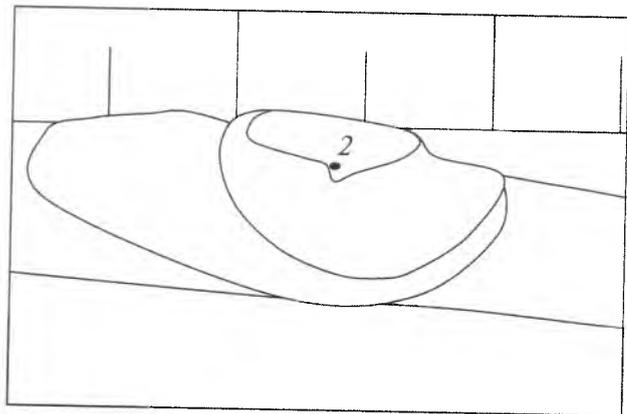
Пора в стыковом сварном соединении трубопровода. Дефект заметен после удаления избыточной выпуклости сварного шва абразивным инструментом
